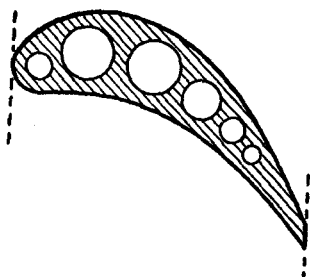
Querschnitt einer Turbinenschaufel mit Wasserkühlung
